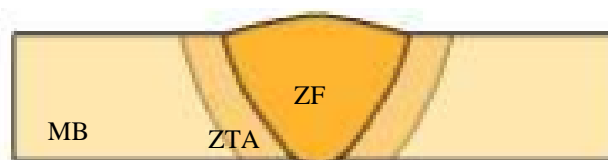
Representação esquemática das regiões da junta soldada. MB = metal base; ZTA = Zona termicamente afetada; ZF = Zona Fundida.
